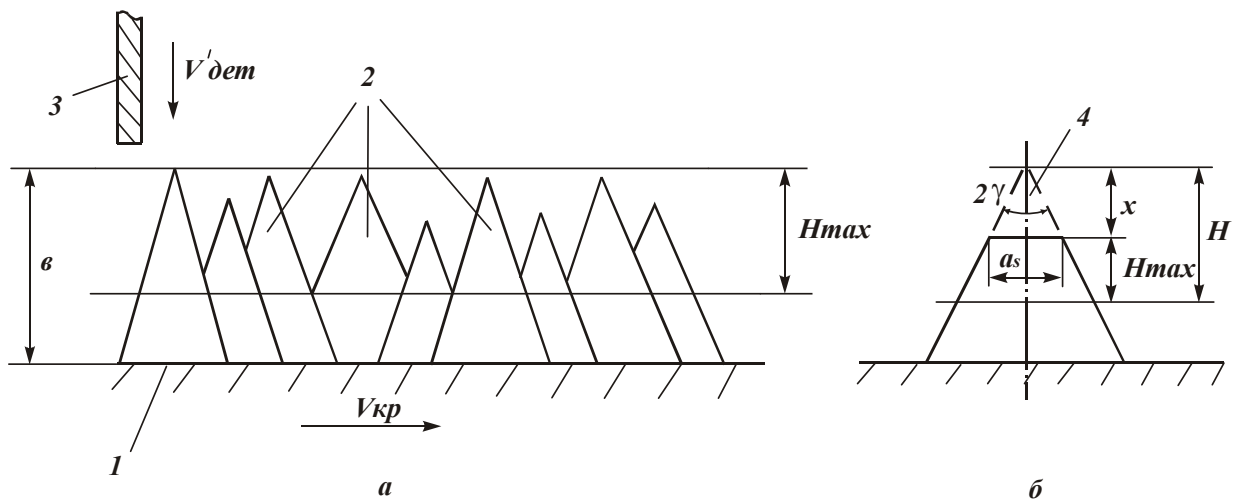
Расчетные схемы шлифования: 1 – связка круга; 2 – режущие зерна; 3 – обрабатываемая пластинка; 4 – изношенная часть зерна.
